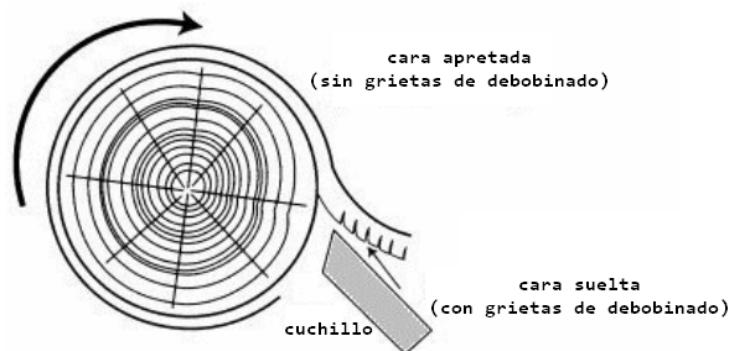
Lado apretado y lado suelto de la chapa, aparición de grietas de desbobinado (Marchal *et al.* 2009).
